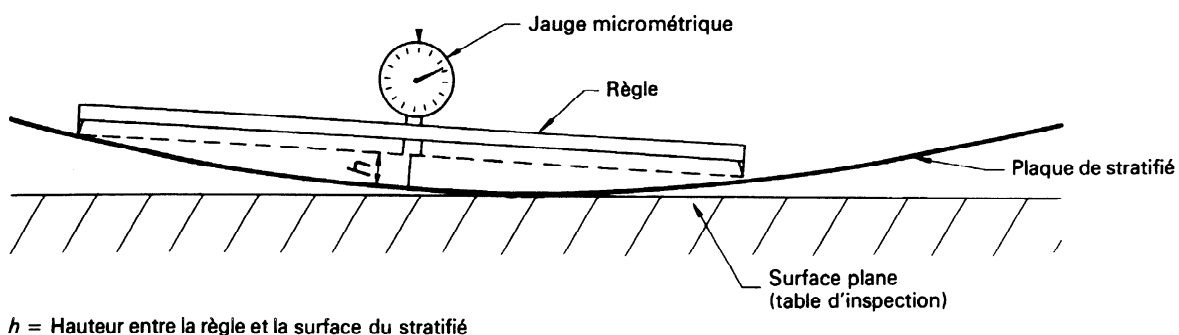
Exemple d'équipement pour le mesurage de la planéité (voir 5.2.1)
